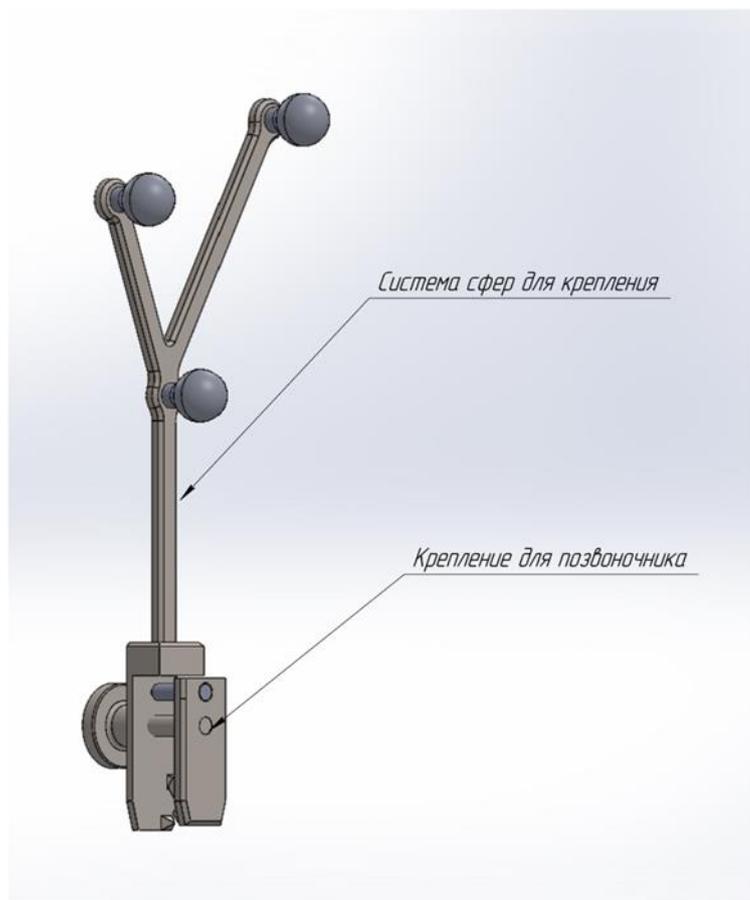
Общий вид крепления для позвоночника в сборе
